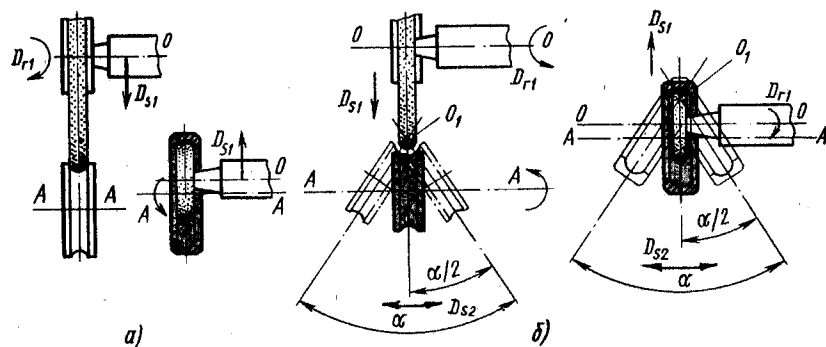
Движения подачи при шлифовании врезанием (а) и методом качения заготовки или круга (б) дорожек качения подшипников
